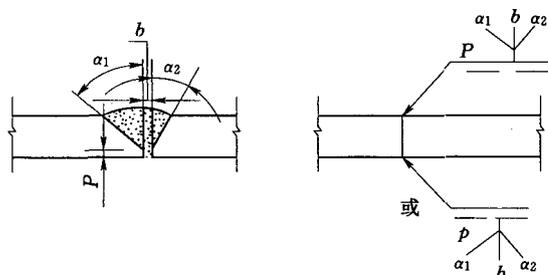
单面带双边不对称坡口焊缝标注
